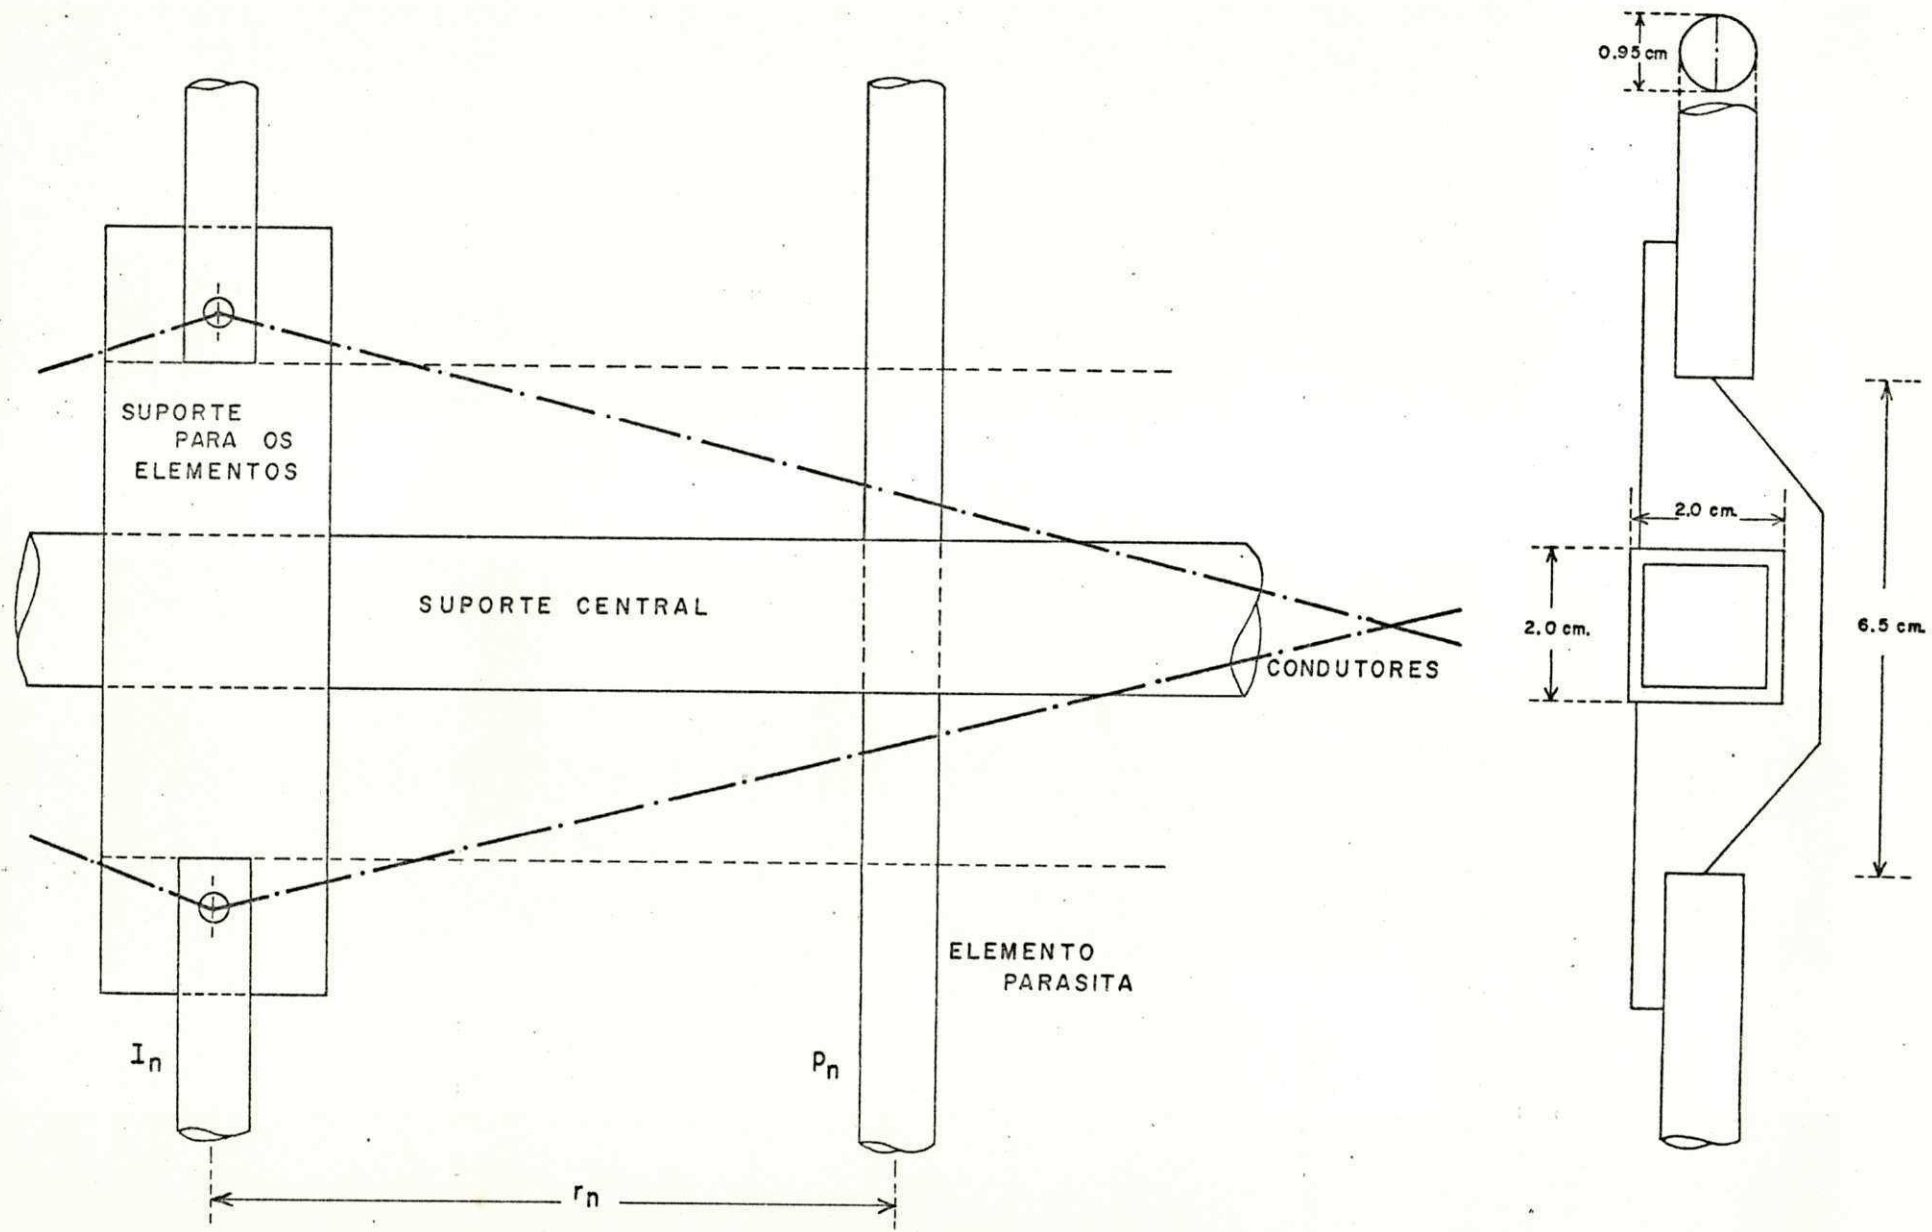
Detalhes de Construção da Antena Y VC-19
